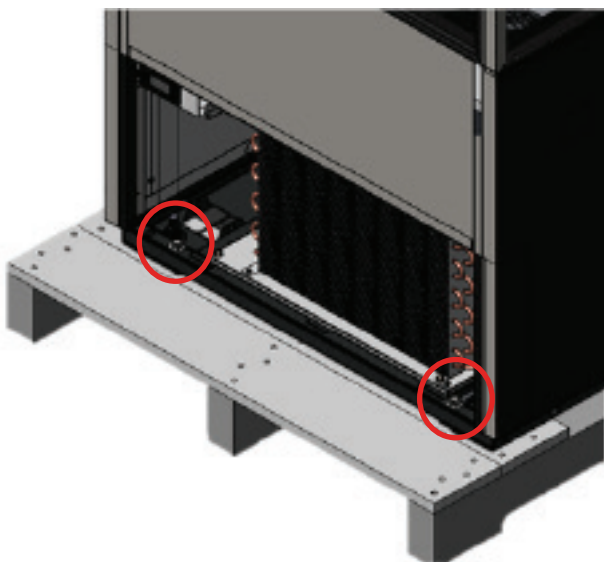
Palettenschrauben vorne und hinten entfernen.
